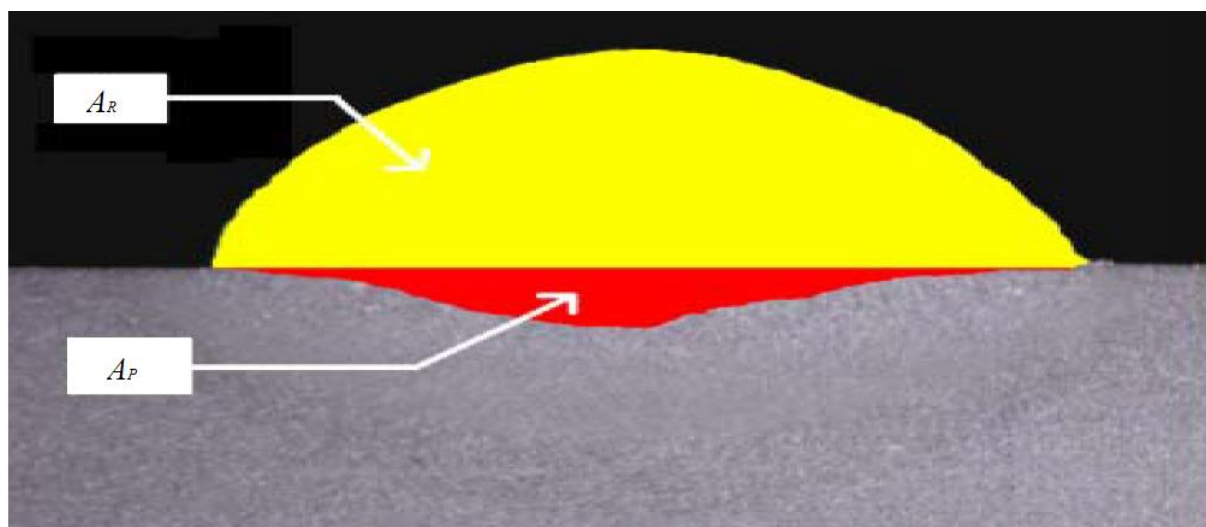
Stupanj miješanja za različite postupke zavarivanja [9]
